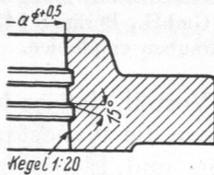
Kegelige Flanschbohrung an Walzflanschen.
